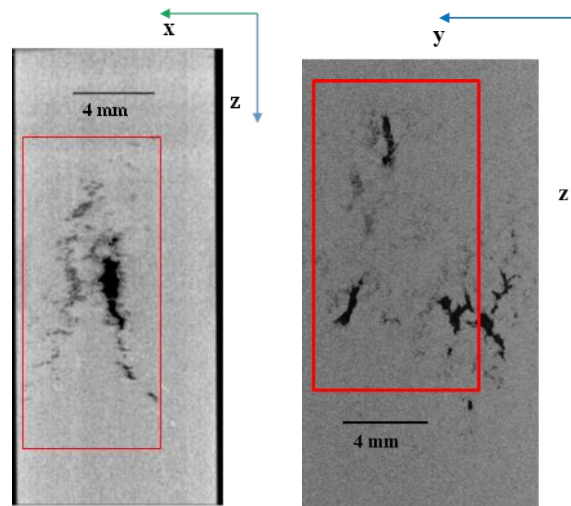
Coupes représentant les retassure interne de la zone d'extraction. A gauche sur le plan xOz et à droite sur le plan yOz
